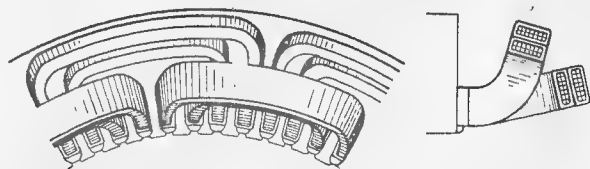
Внешний вид обмотки трехфазного тока с лобовыми частями в двух ярусах
